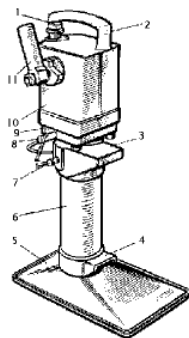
Домкрат ПДР-8 [7]: 1 – пробка с отверстием (сапун); 2 – ручка для переноски домкрата; 3 – несъемное приспособление для рихтовки; 4 – грузоподъемная лапа; 5 – опорная плита; 6 – цилиндр; 7 – стопорный винт; 8 – спускной вентиль; 9 – клапанная коробка; 10 – резервуар для масла; 11 – рукоятка насоса (съемный стержень не показан)
